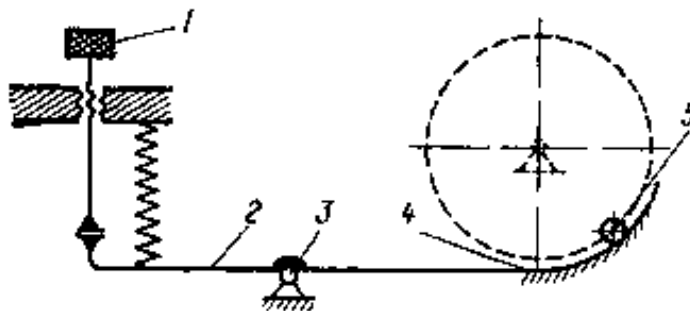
Схема механізму регулювання маси тістових заготовок РМК-60
